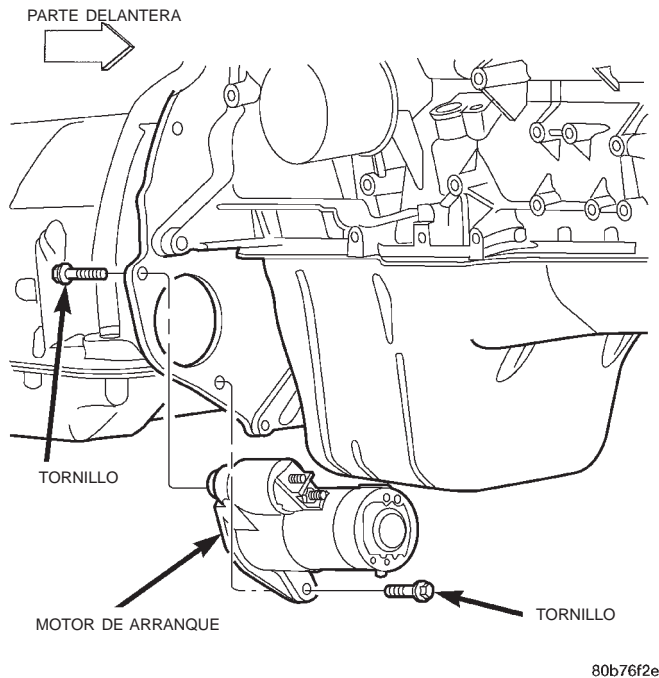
Desmontaje e instalación del motor de arranque-motor 4.0L
